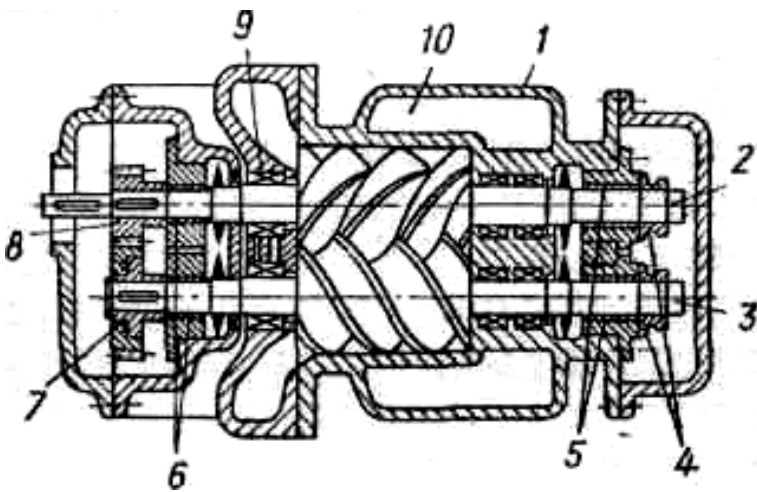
Схема гвинтового компресора: 1- корпус; 2 - ведучий гвинт; 3 - відомий гвинт; 4 - напольгливий підшипник; 5, 6 - опорні підшипники; 7, 8-синхронізуючі шестерні; 9 - ущільнення; 10 - порожнина для циркуляції охолоджуючої рідини
